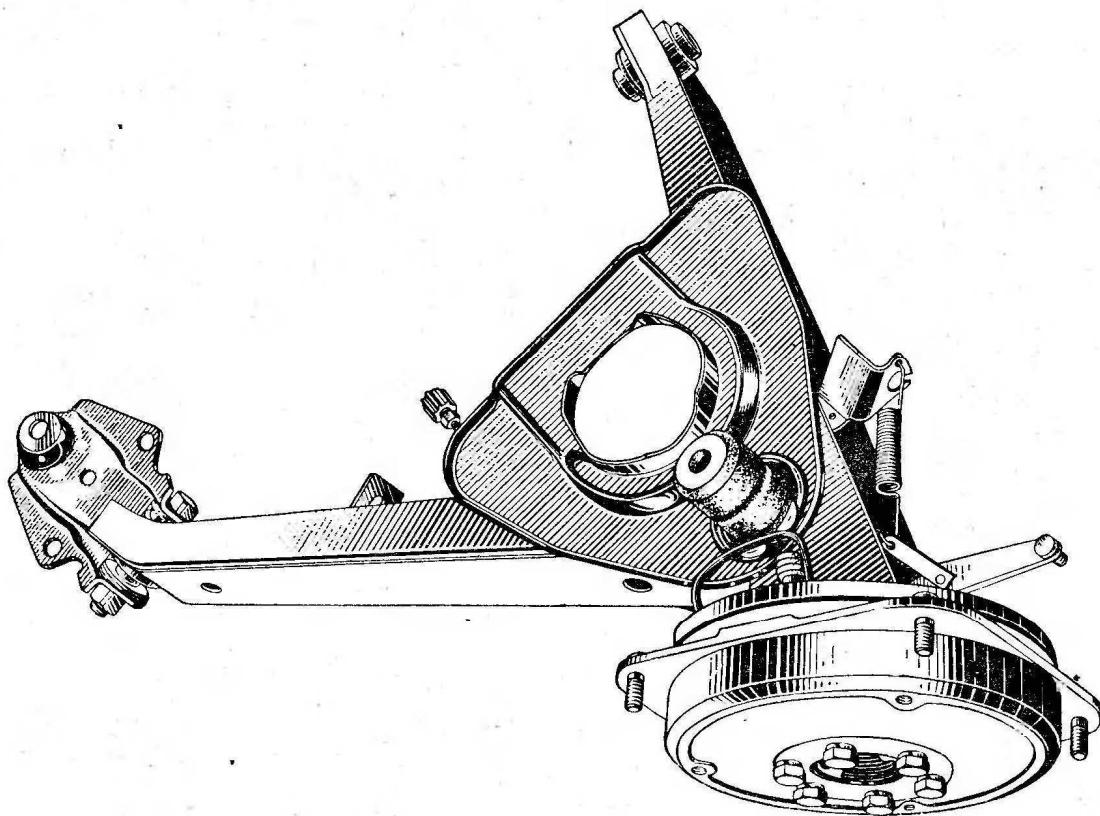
Hebel der Hinterradaufhängung, komplett mit Bremse
